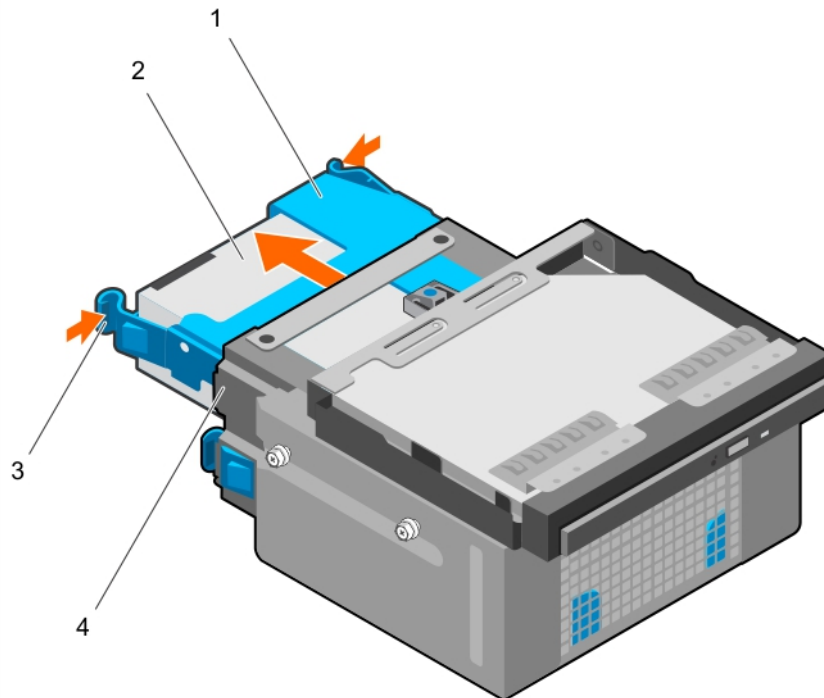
Entfernen eines Laufwerksträgers aus einem Laufwerksgehäuse
